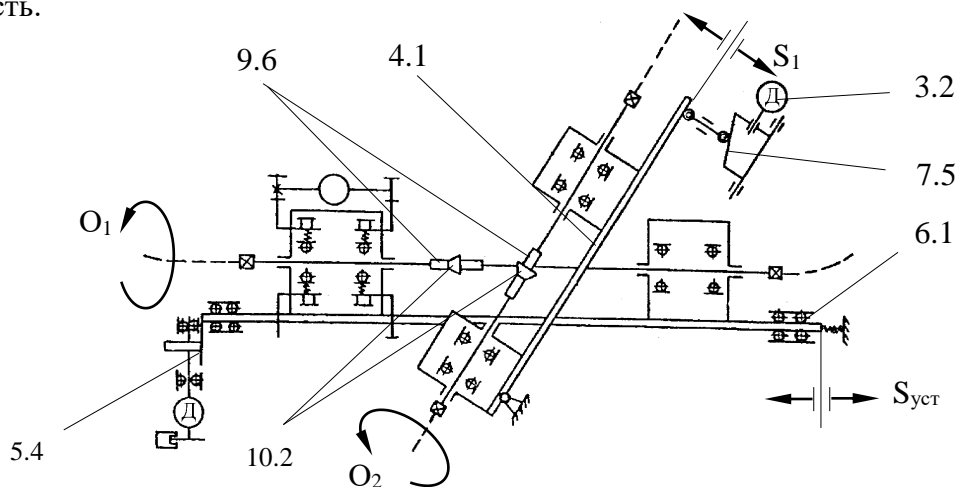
Схема супорт-шпindelь верстата з вісями алмаза-заготовки і алмаза-інструмента, що перетинаються
